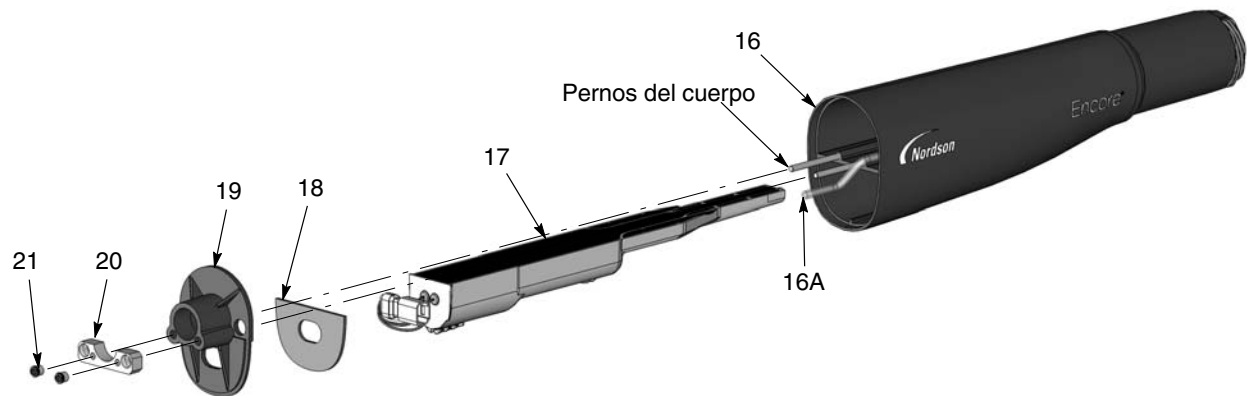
Desmontaje de la pistola - Sustitución de la fuente de alimentación
